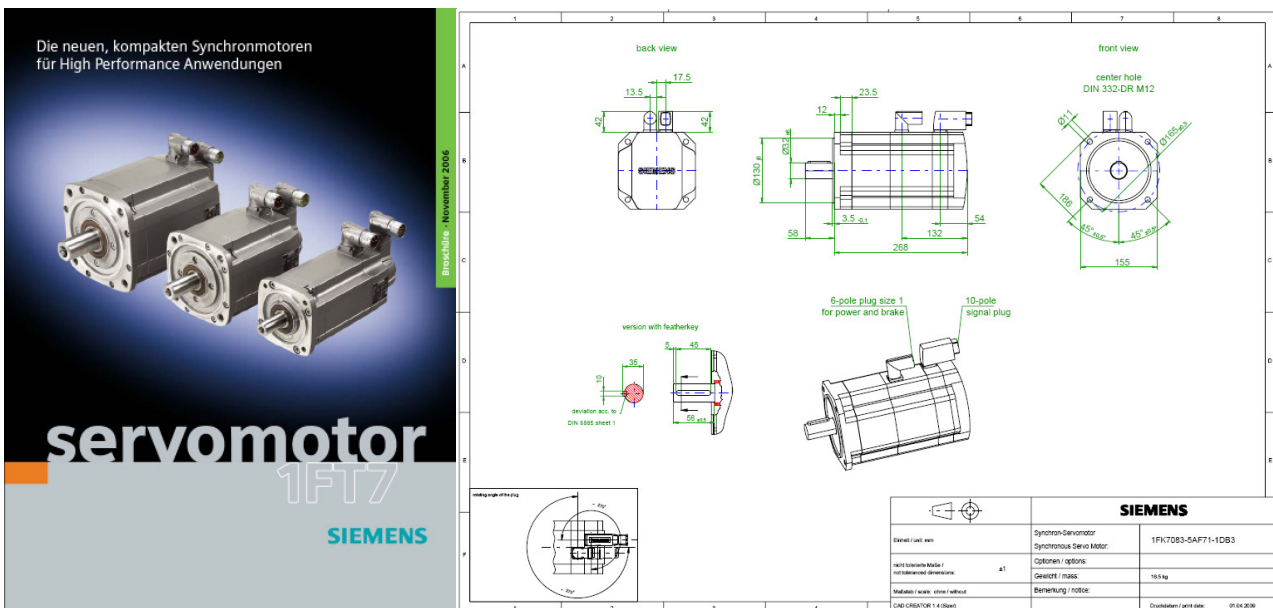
luftgekühlter Motor 1FK7083-5AF71
